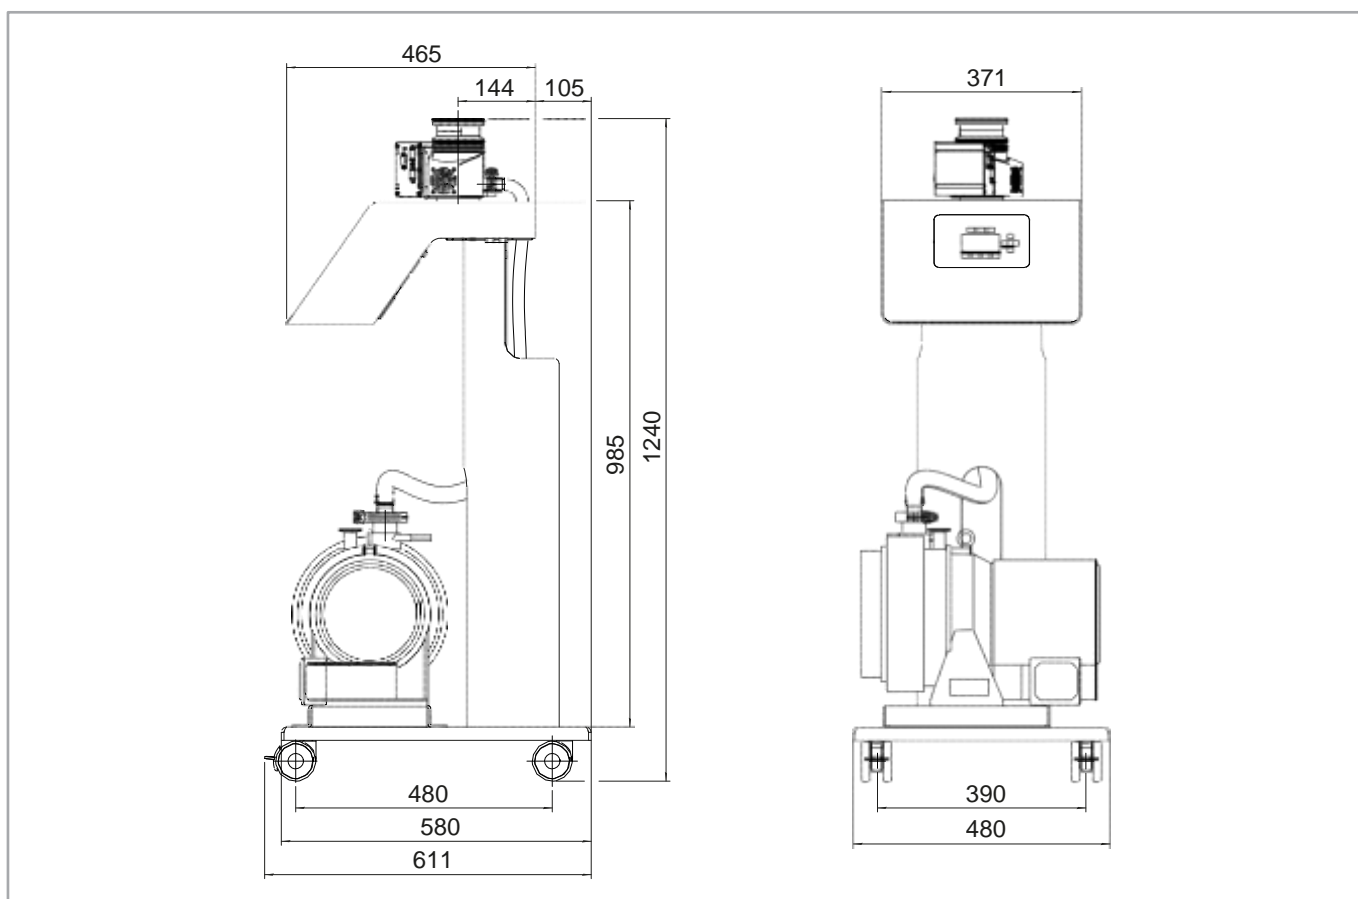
Габаритные размеры TURBOLAB 80 Cart, размеры в мм
